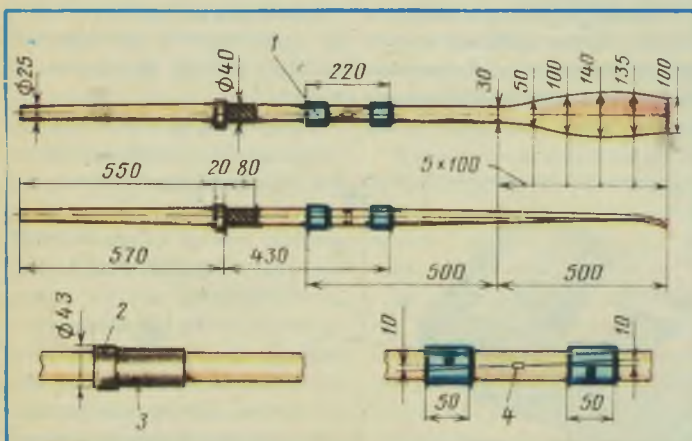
Весло: 1 — металлические кольца; 2 — каблук (кожа, резина); 3 — манжета (кожа, резина); 4 — шпонка.
